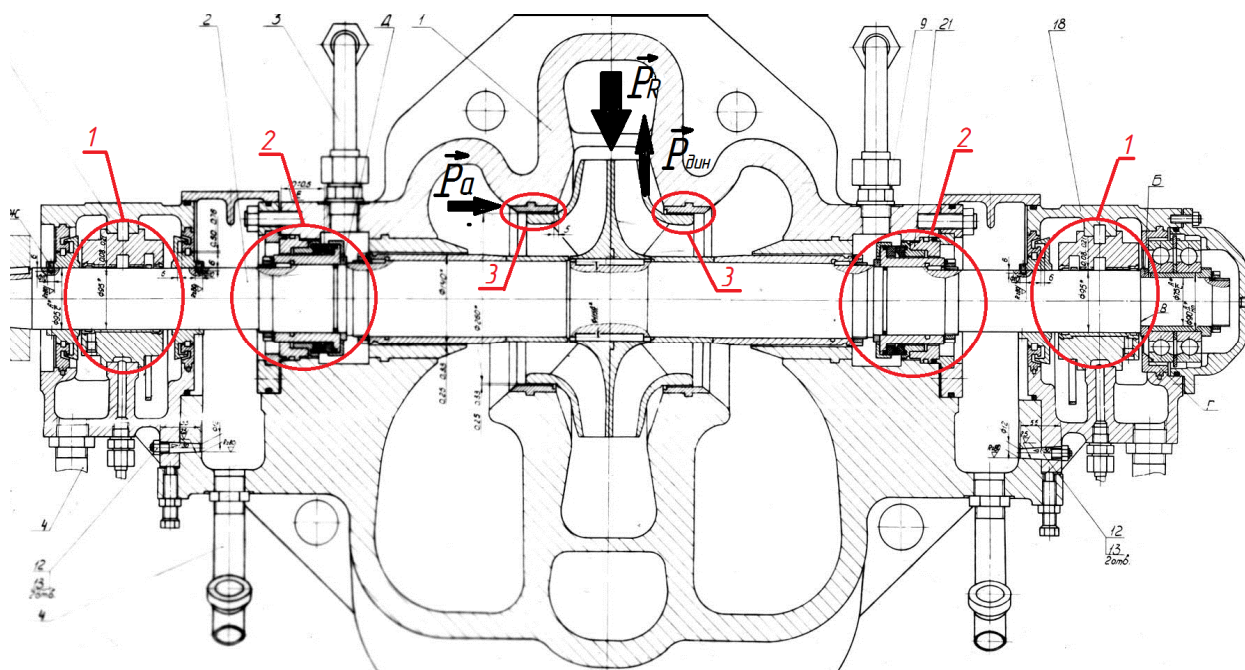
Основные изнашивающиеся узлы и схема нагружения ротора насоса тип НМ: 1 – подшипники скольжения; 2 – торцевые уплотнения ротора; 3 – щелевые уплотнения рабочего колеса.
